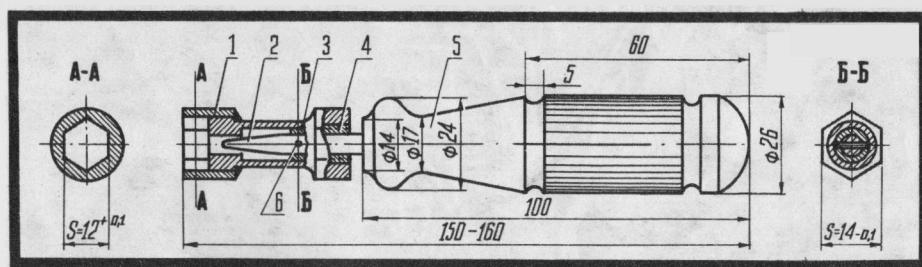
Ключ-отвертка: 1 — корпус; 2 — отвертка; 3 — упорное кольцо; 4 — заглушка; 5 — рукоятка; 6 — штифт.
